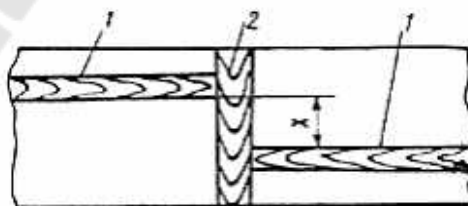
Схема сварки труб с продольным швом:
